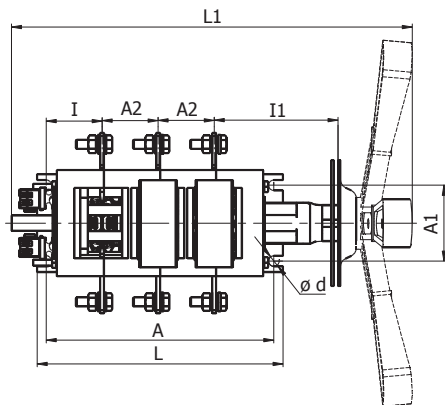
Выключатель-разъединитель трехполюсный на два направления с боковой смещенной рукояткой.
